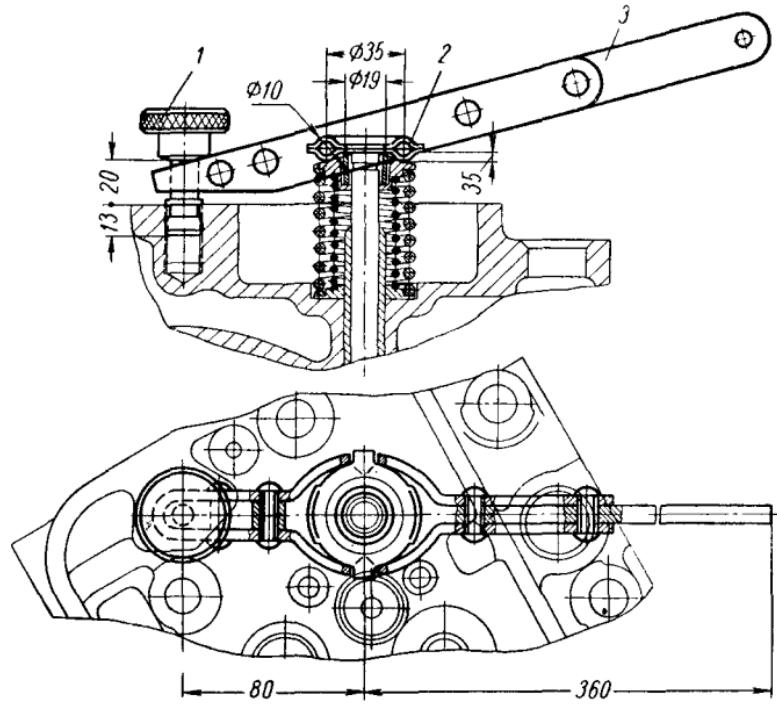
Приспособление для снятия и установки впускных и выпускных клапанов:
